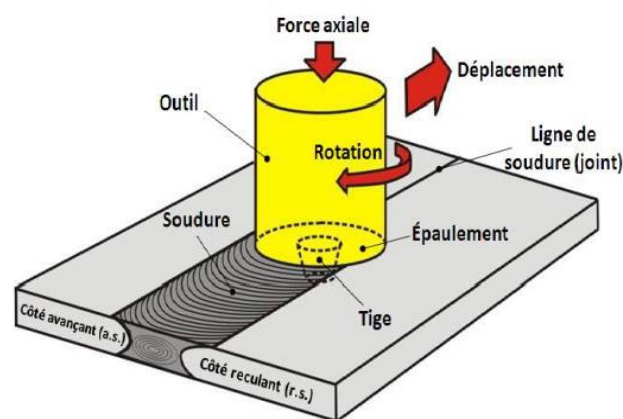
Visualisation des paramètres de soudage [12].
